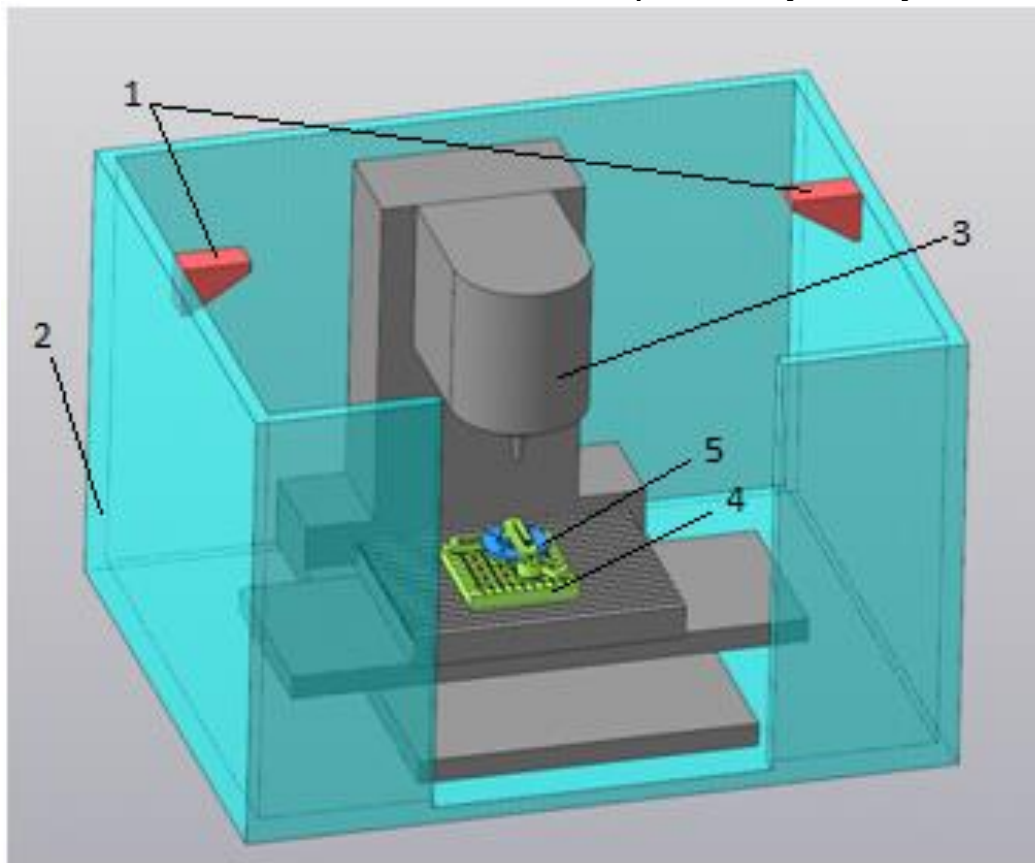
Пример стационарного размещения сканирующих устройств внутри кабинета станка с установленными на нем оснасткой и заготовкой: 1 – сканирующие устройства; 2 – кабинет станка; 3 – станок; 4 – оснастка; 5 – обрабатываемая заготовка;
